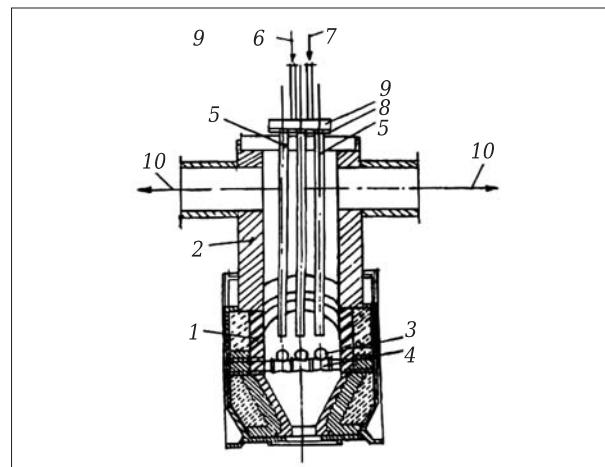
Трехручевая секционная печь СФН со струйно-рекуперативными горелками (СРГ): 1 — кладка; 2 — отводящий канал; 3 — трубные заготовки; 4 — ролик; 5 — корпуса горелок СРГ; 6 — подача газа; 7 — подача воздуха; 8 — газовый коллектор; 9 — воздушный коллектор; 10 — отвод дымовых газов
